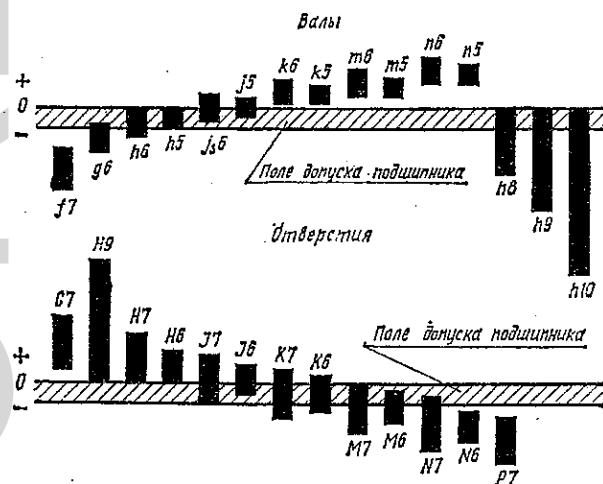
Схема расположения полей допусков валов и отверстий для различных посадок
